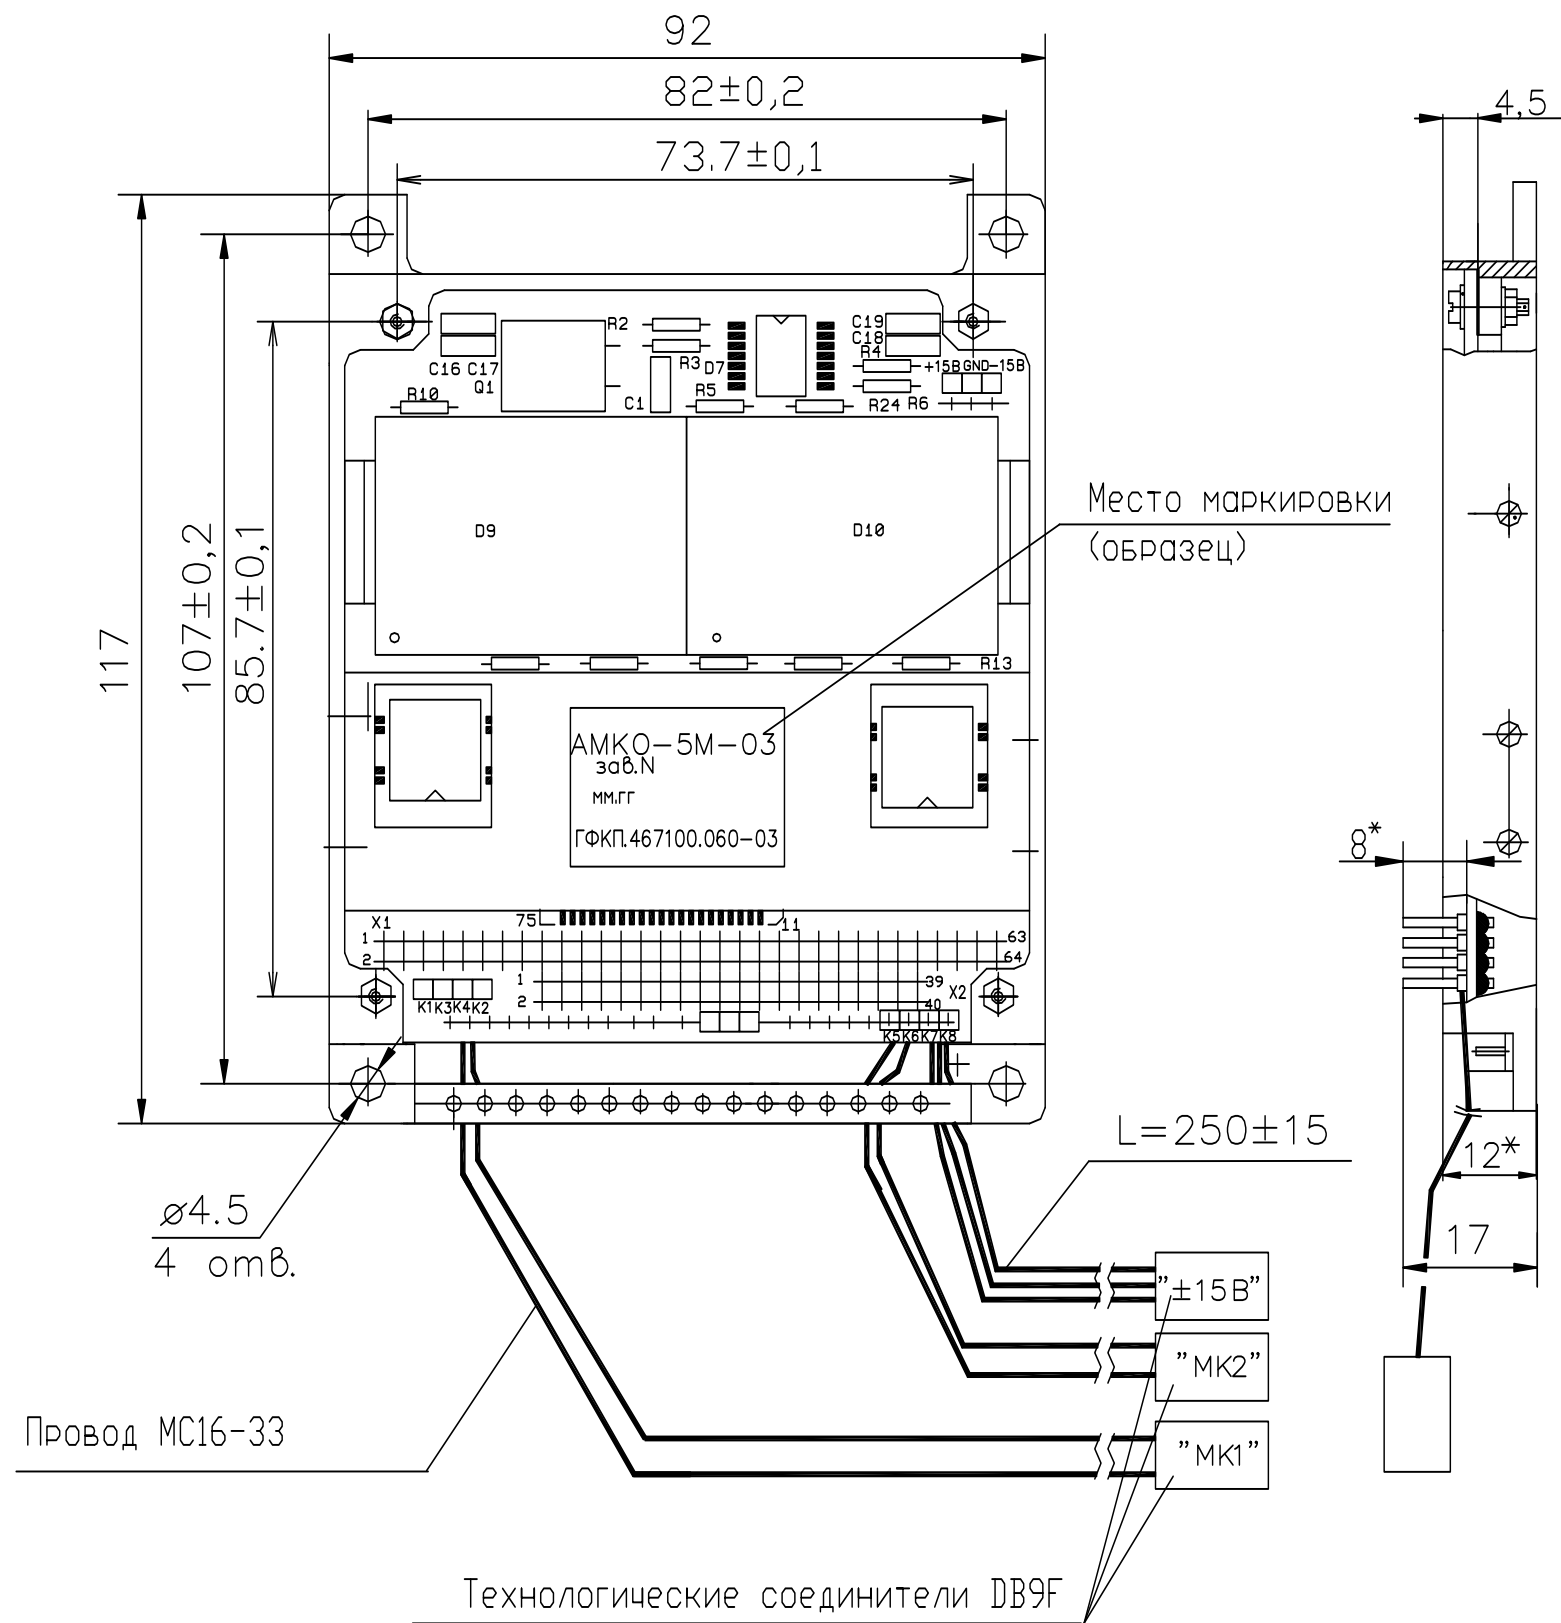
Габаритный чертеж исполнения АМКО-5М-03
